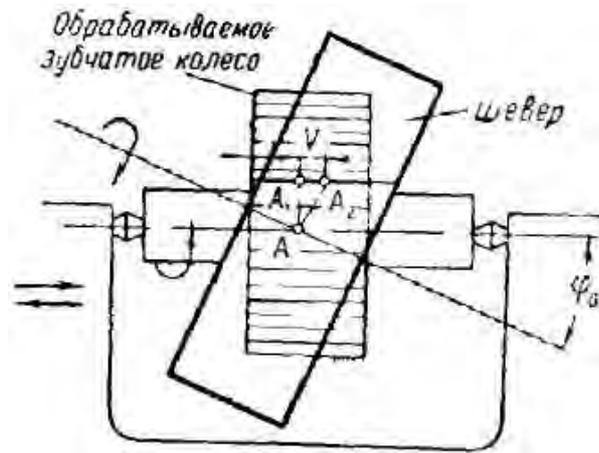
Схема обработки зубчатого колеса дисковым шевром
